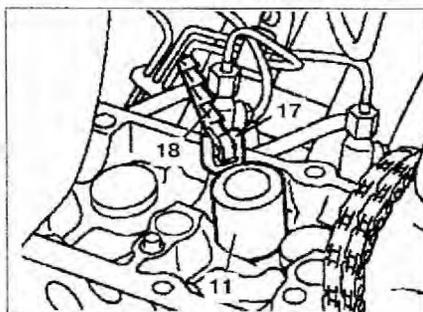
Вставьте направляющую втулку 11 в отверстие под гидрокомпенсатор, вкрутите фиксатор с опорным подшипником с фиксирующей вилкой 17 в резьбовое отверстие болта крепления крышки и совместите их.
